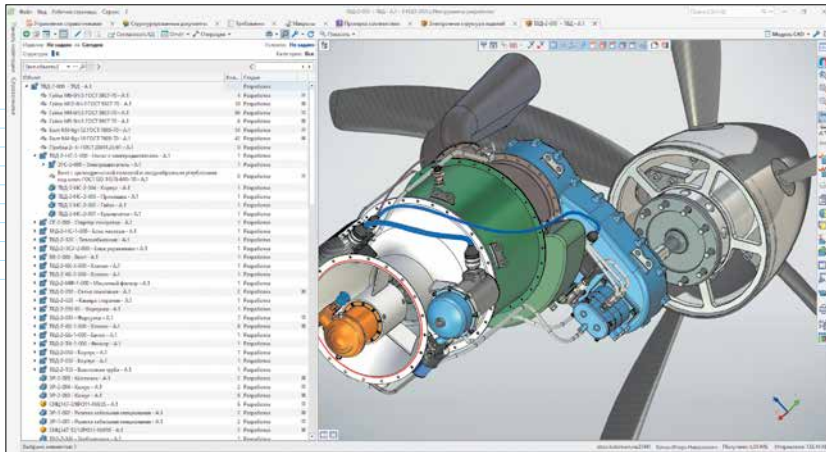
Пример сборочной единицы – двигательная установка с винтом для БПЛА
